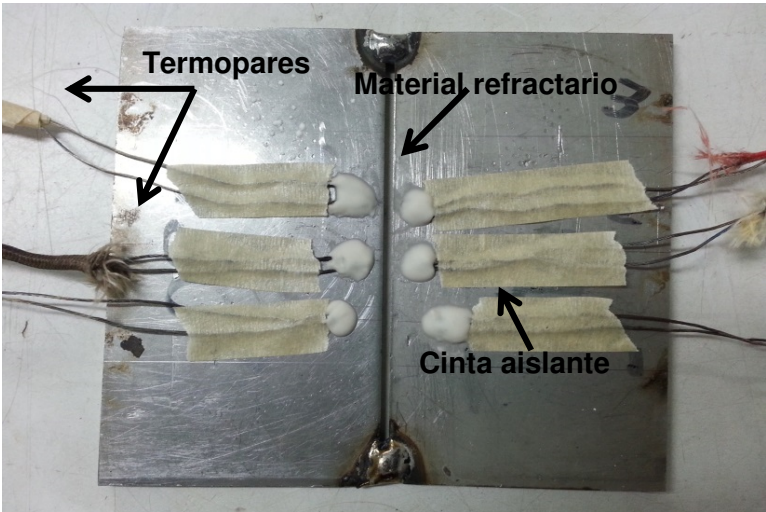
Placas de Aceros AISI 430 Y AISI 316L preparadas para ser soldadas
